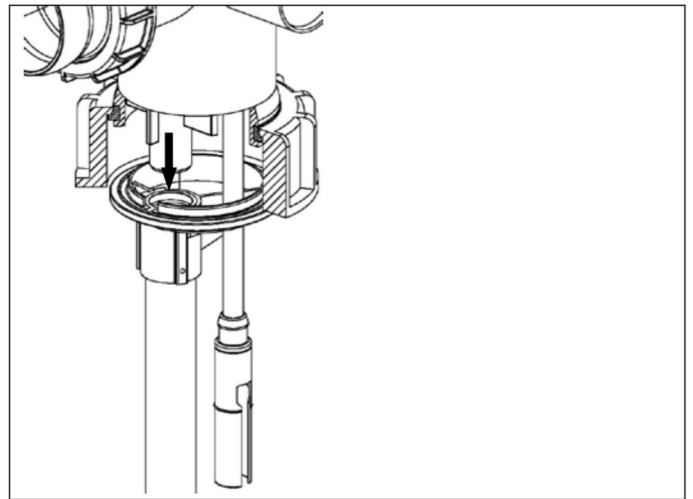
Montage Grundeinheit auf Flansch des Teleskopschaumrohrs
